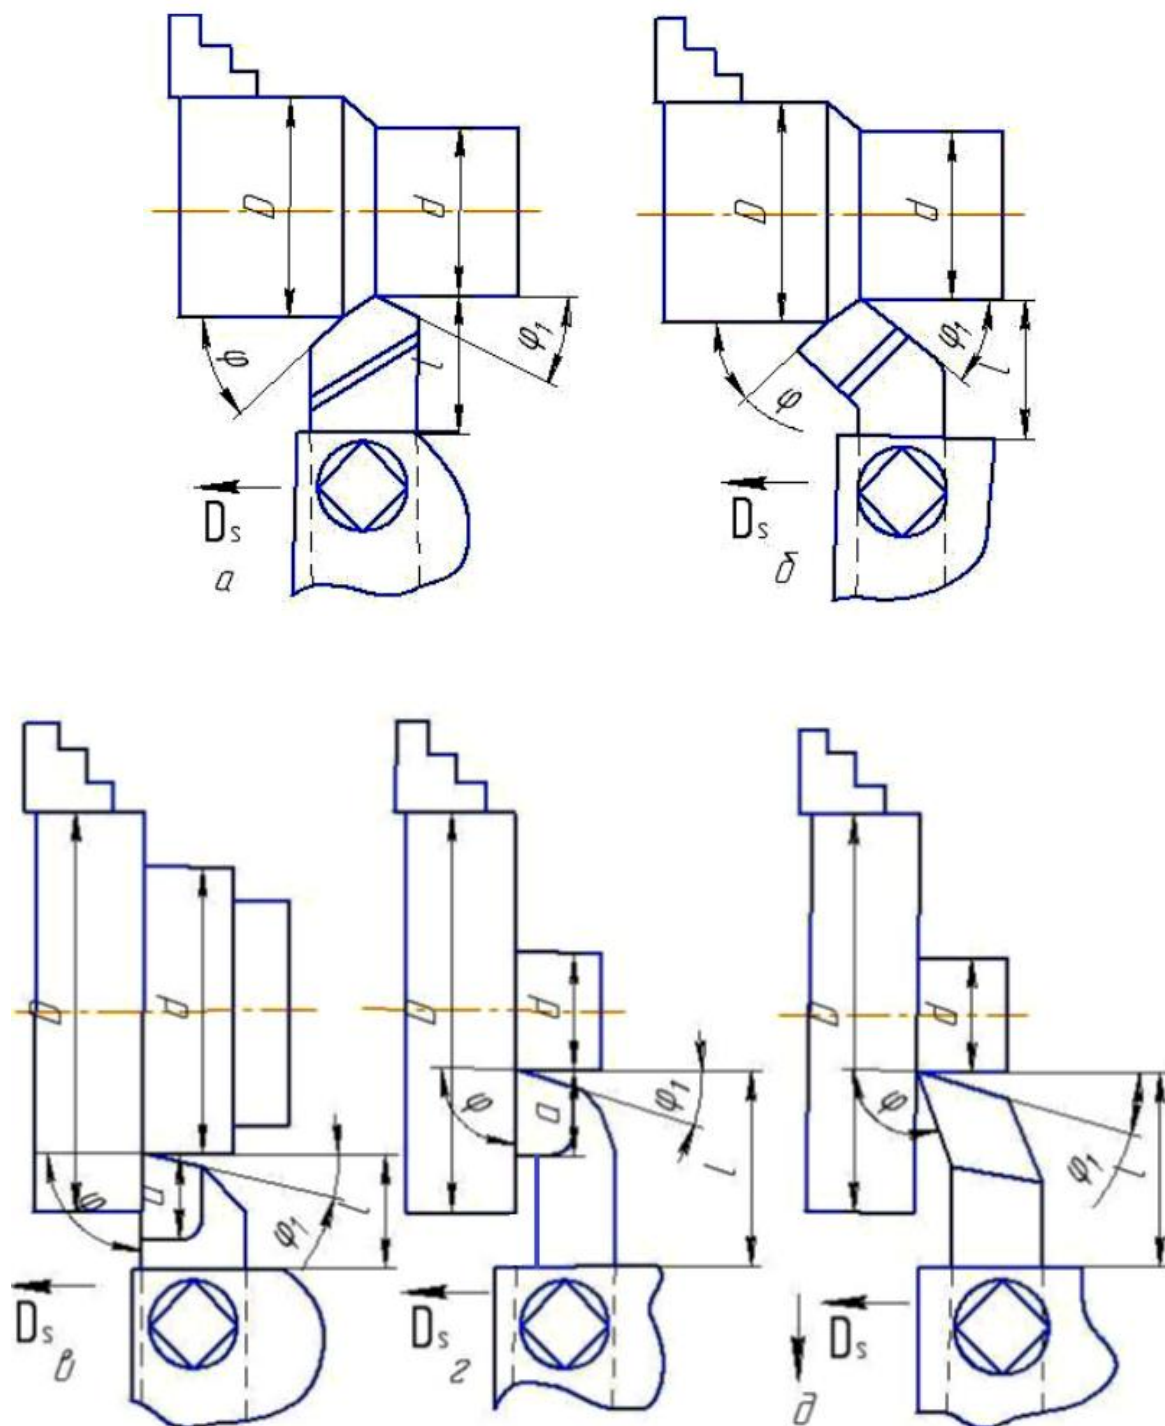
Резцы для обточки: а – прямой проходной;
